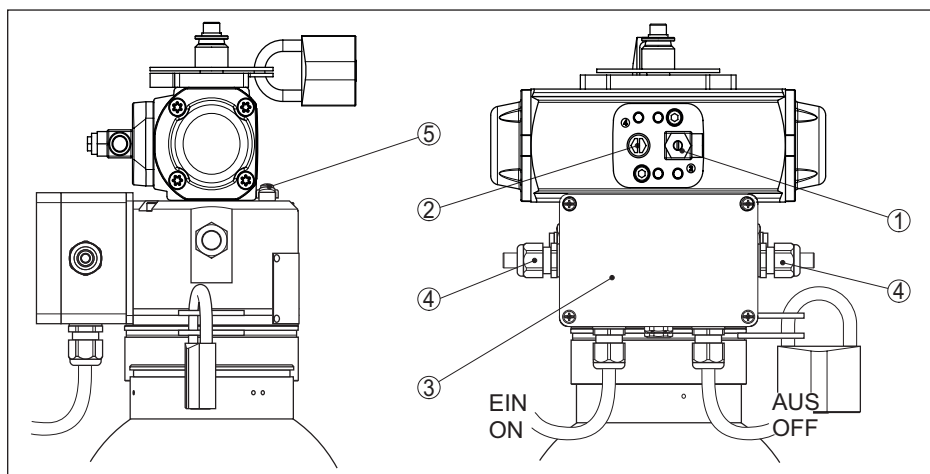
Raccordement des conduites d'air comprimé sur le VEGASOURCE 35 - Version K, M
